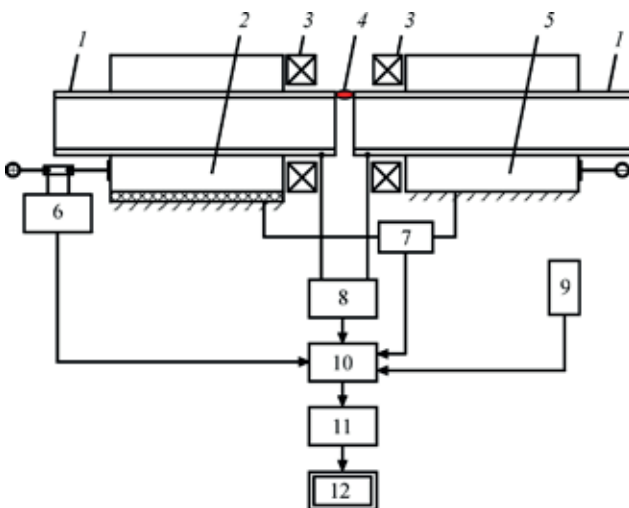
Блок-схема макету контролю якості зварюваних з'єднань: 1 – зварювані труби; 2 – рухомий затискний пристрій; 3 – елементи магнітної системи; 4 – стовп електричної дуги, яка рухається по кромках зварюваних труб; 5 – нерухомий затискний пристрій; 6 – датчик струму з інструментальним підсилювачем сигналу; 7 – датчик положення рухомої частини зварювальної установки; 8 – датчик падіння напруги на зварювальній дузі; 9 – датчик вимірювання абсолютного тиску гідравлічної системи, вбудований в штокову порожнину циліндру осадка зварювальної машини; 10 – нормуючий інструментальний підсилювач (з ФНЧ $F_{\text{зп}} = 100$ Гц); 11 – приймач аналогово-цифровий перетворювач (АЦП); 12 – персональна електронно-обчислювальна машина
